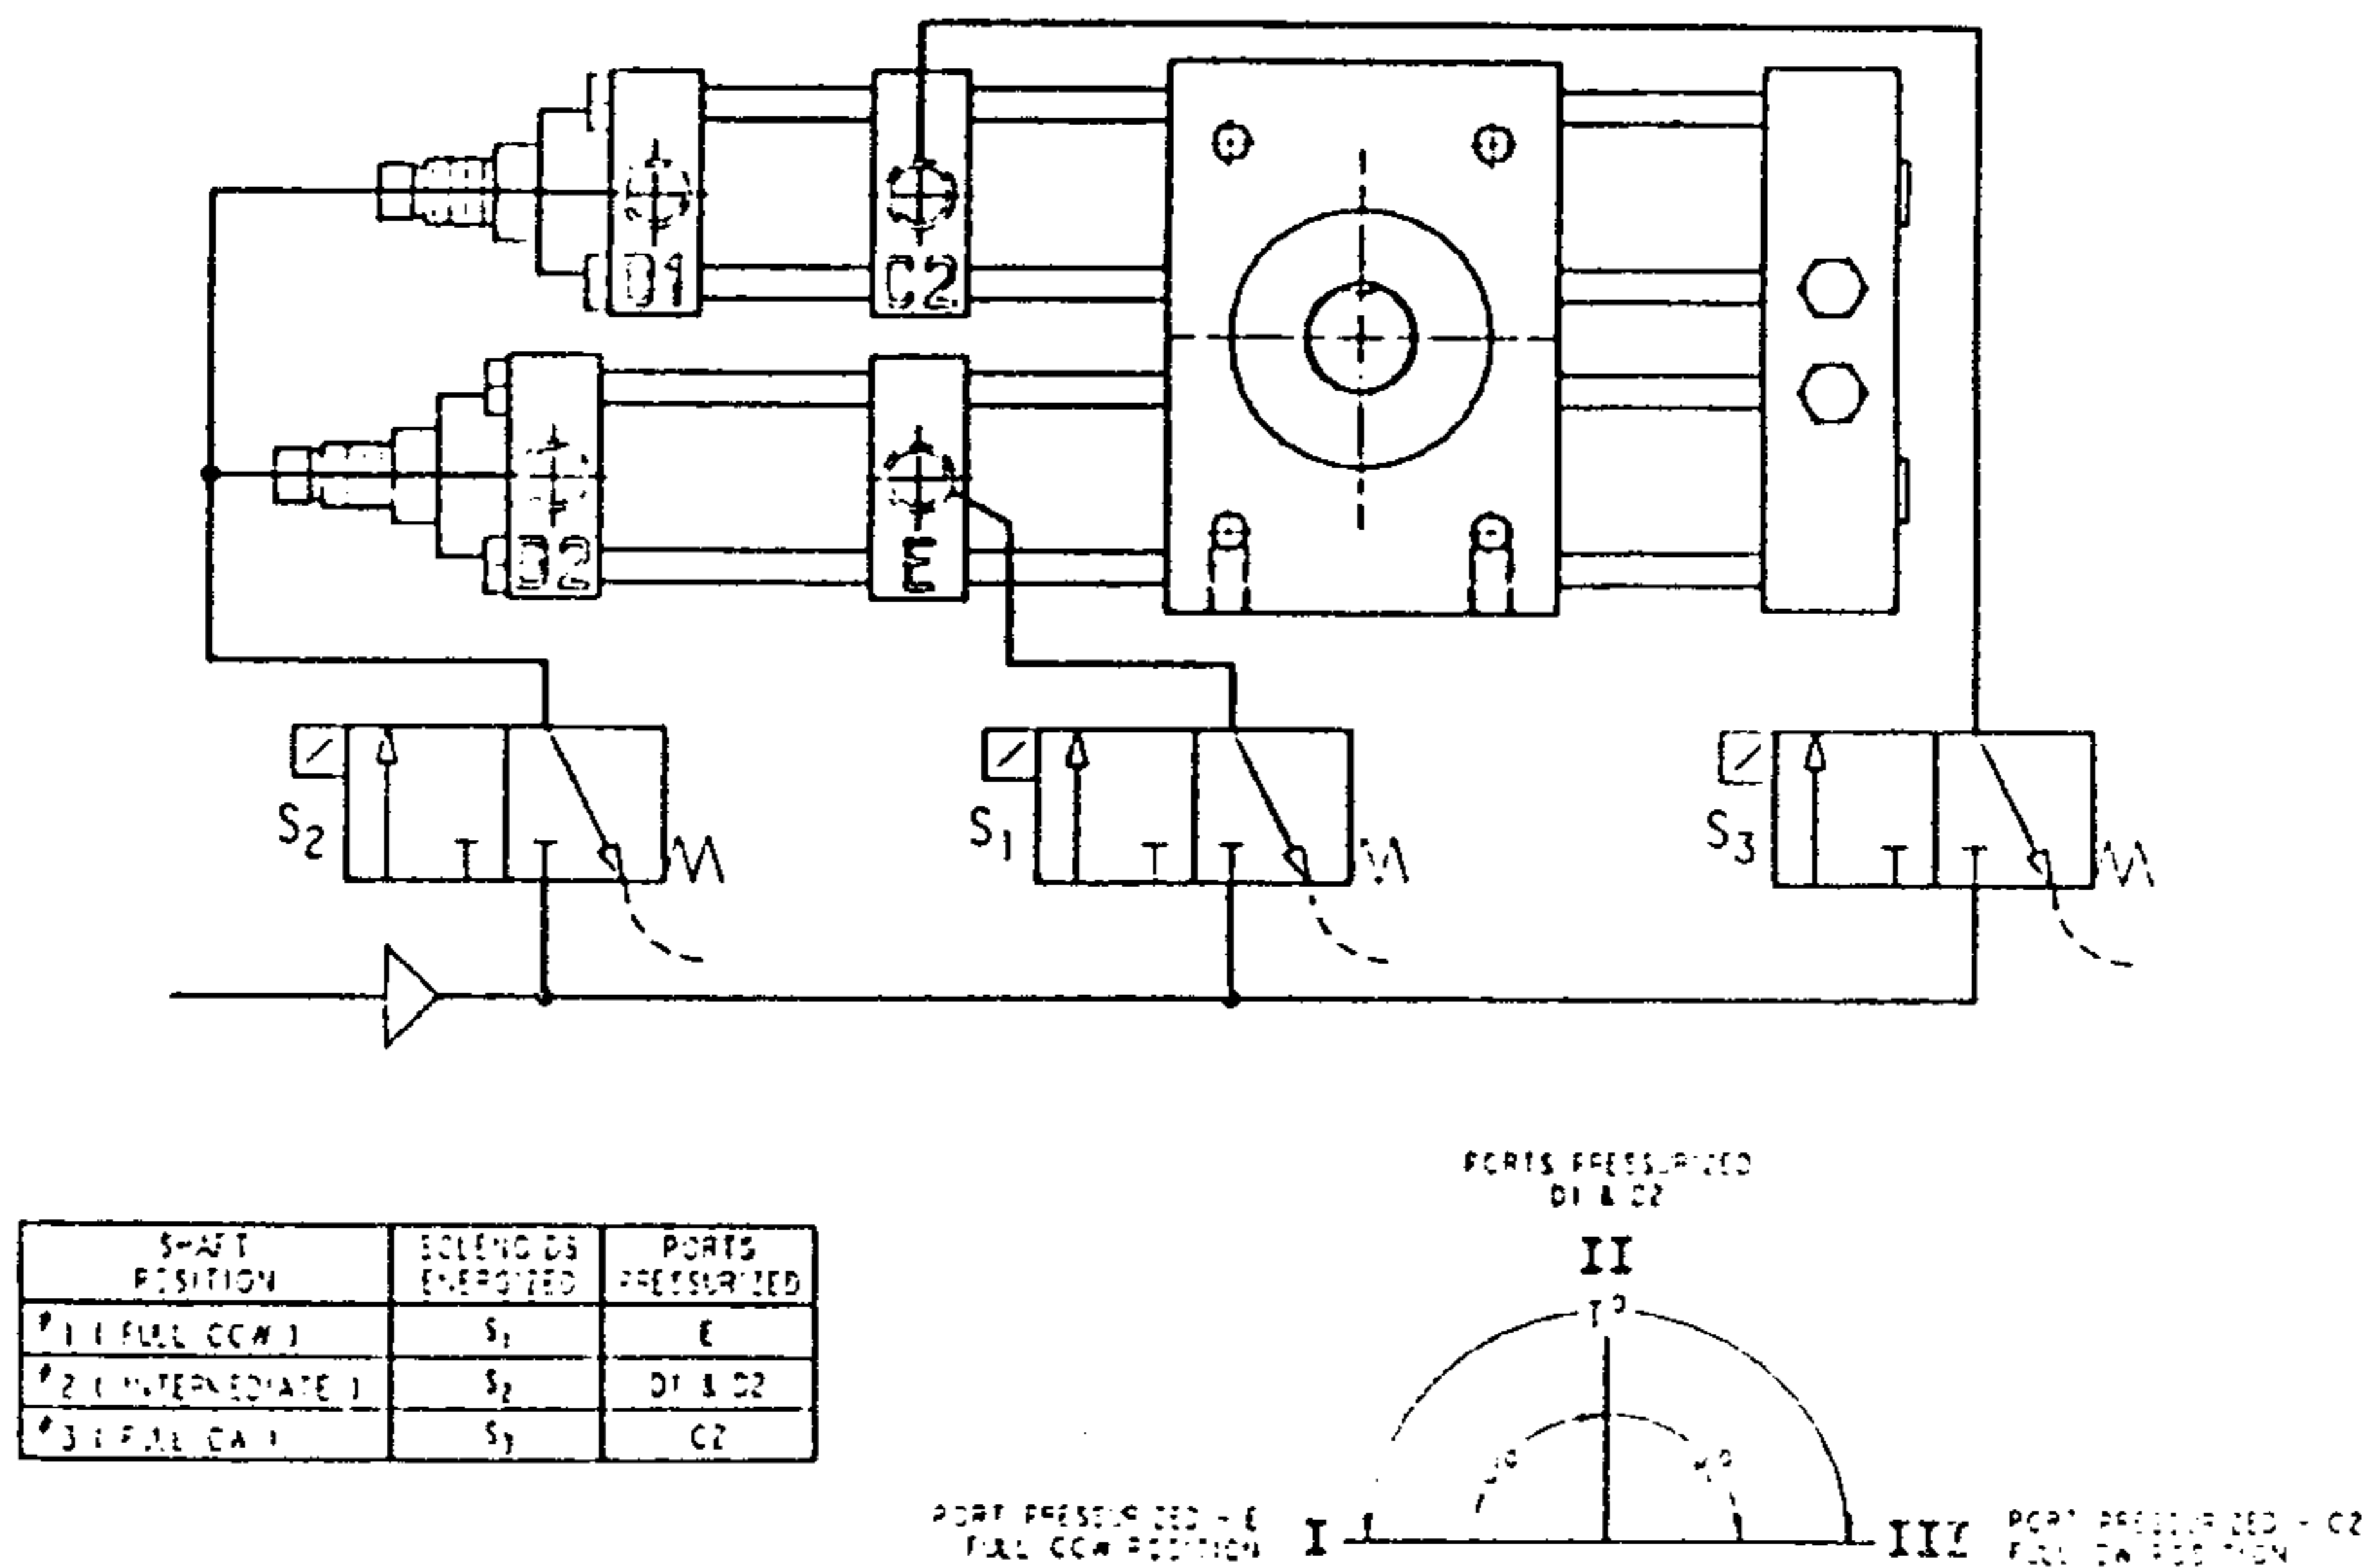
3-Position Rotary Actuator with Air Oil Tandem Units
